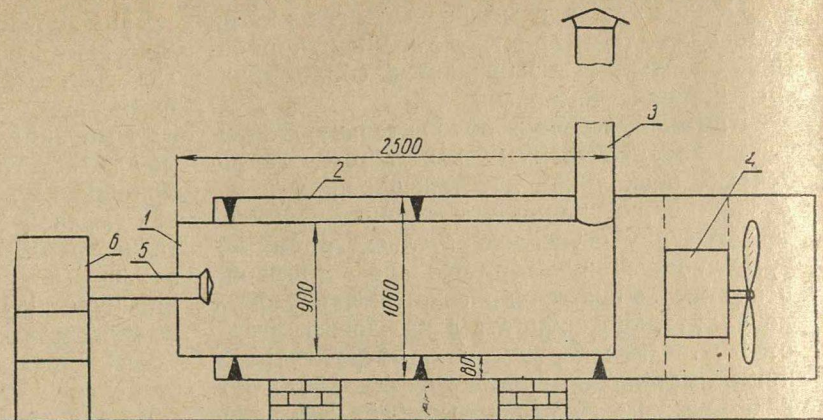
Схема воздухоподогревателя (размеры в миллиметрах): 1—камера сгорания; 2—вытяжная труба; 4—вентилятор; 5—горелка; 6—приспособление ПНГ—ВИЭСХ.
